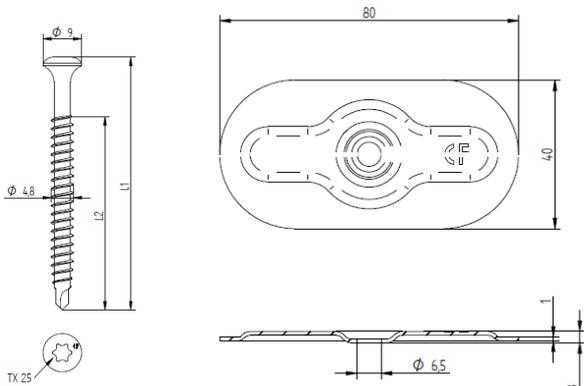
Vis EUROFAST EDS-B 4,8 + plaquette de fixation EUROFAST DVP-EF-8040
